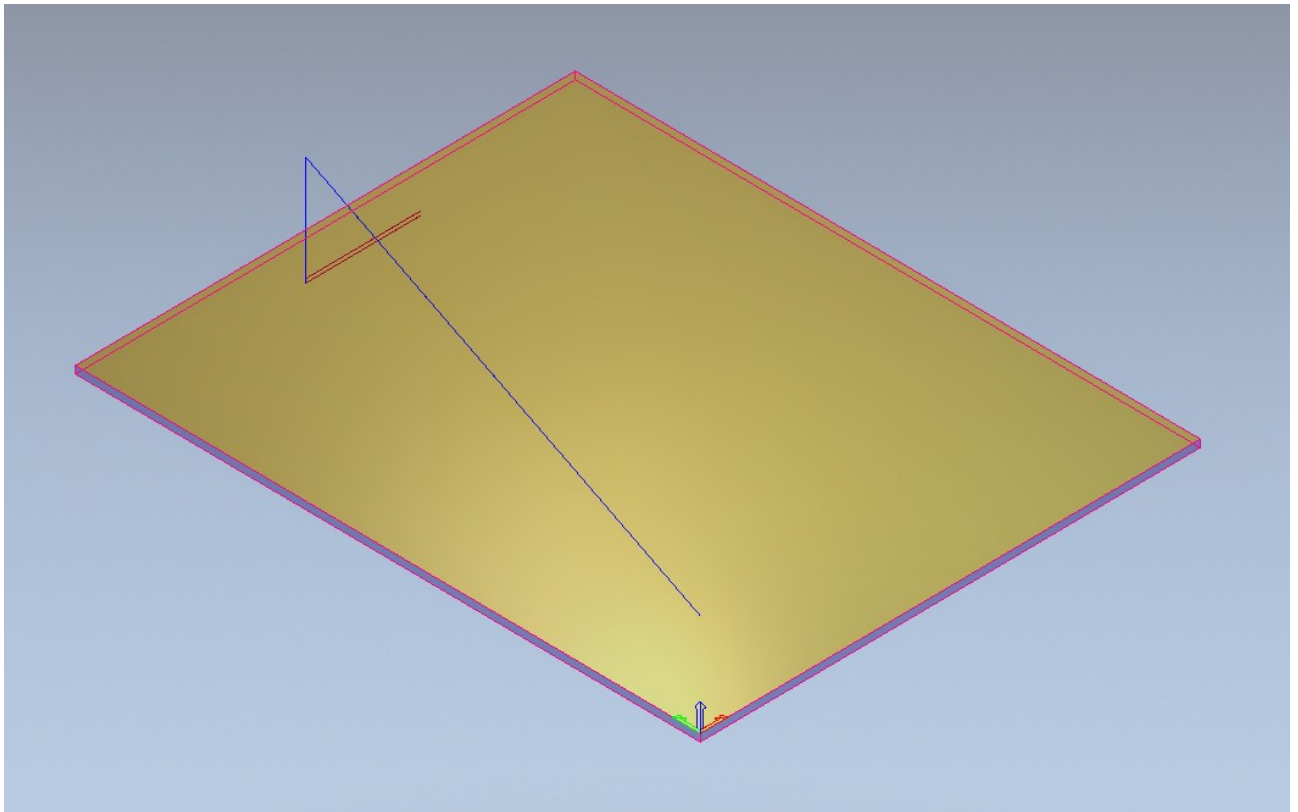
Траекторія руху інструмента на фрезерування пазу
